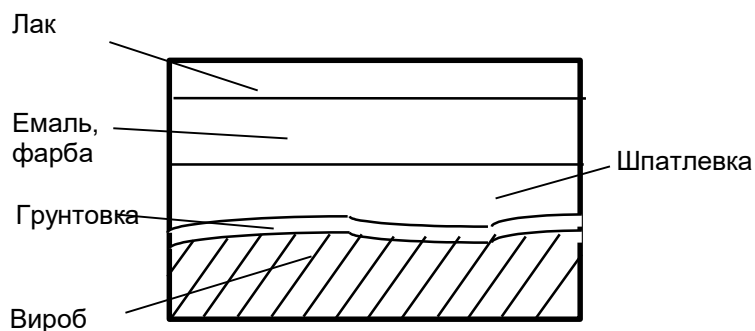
Схема лакофарбового покриття металевих конструкцій
